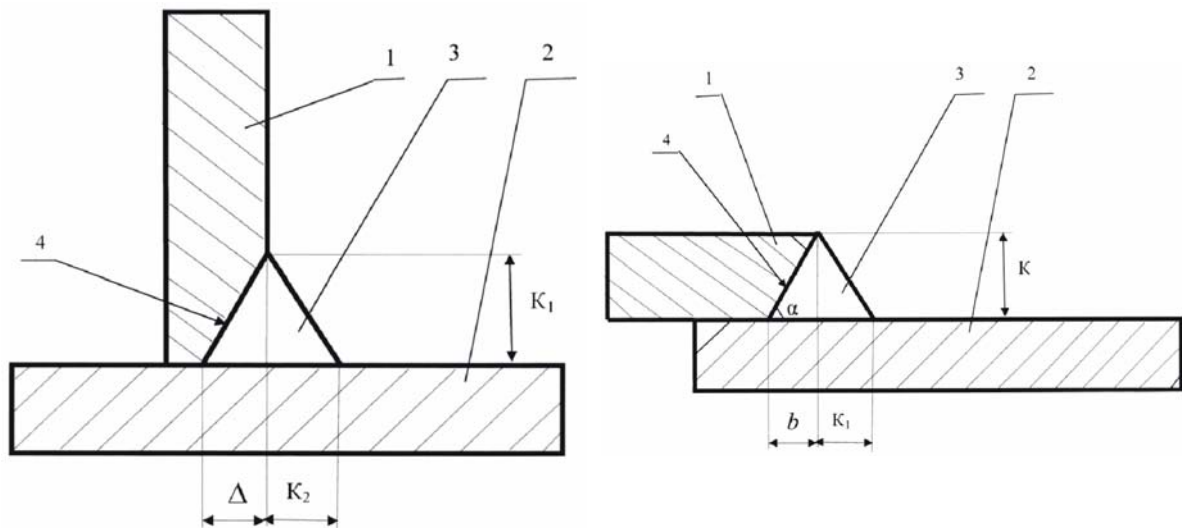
Схема таврового (а) и нахлесточного (б) сварного соединения:
